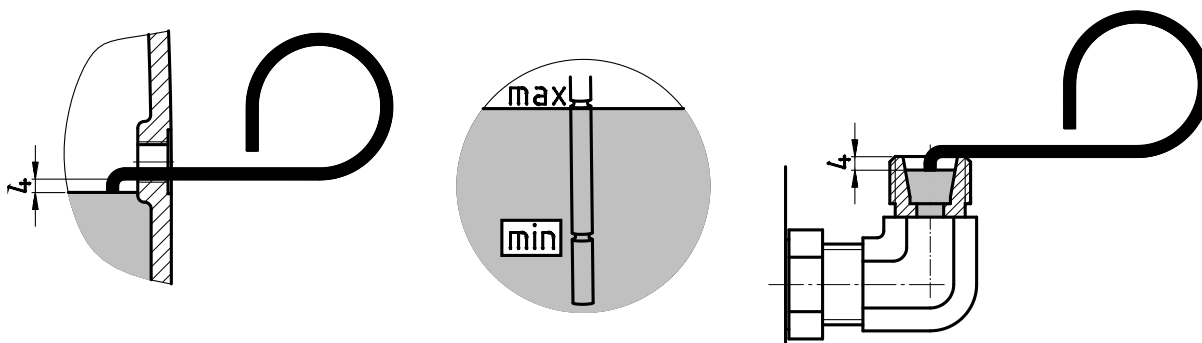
Проверка уровня масла с помощью масломерного щупа
